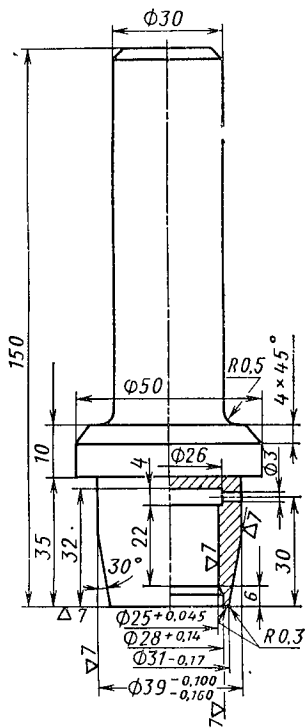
Оправка для напрессовки торцового уплотнения на шип крестовины заднего моста
